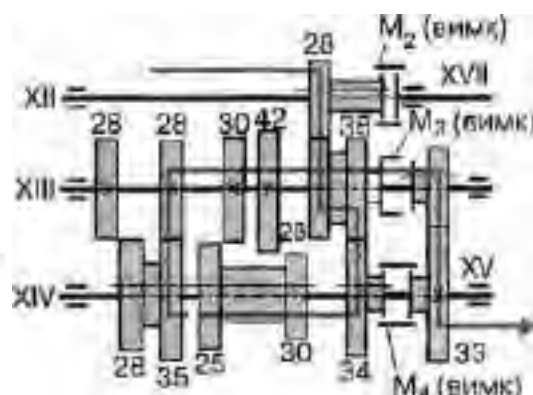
СХЕМА ВАРІАНТА НАСТРОЮВАННЯ ОБОРОТНОГО МЕХАНІЗМУ КОРОБКИ ПОДАЧ ВЕРСТАТА 16К20 НА НАРІЗАННЯ МОДУЛЬНОЇ РІЗЬБИ (ЛАНЦЮГІ А)
